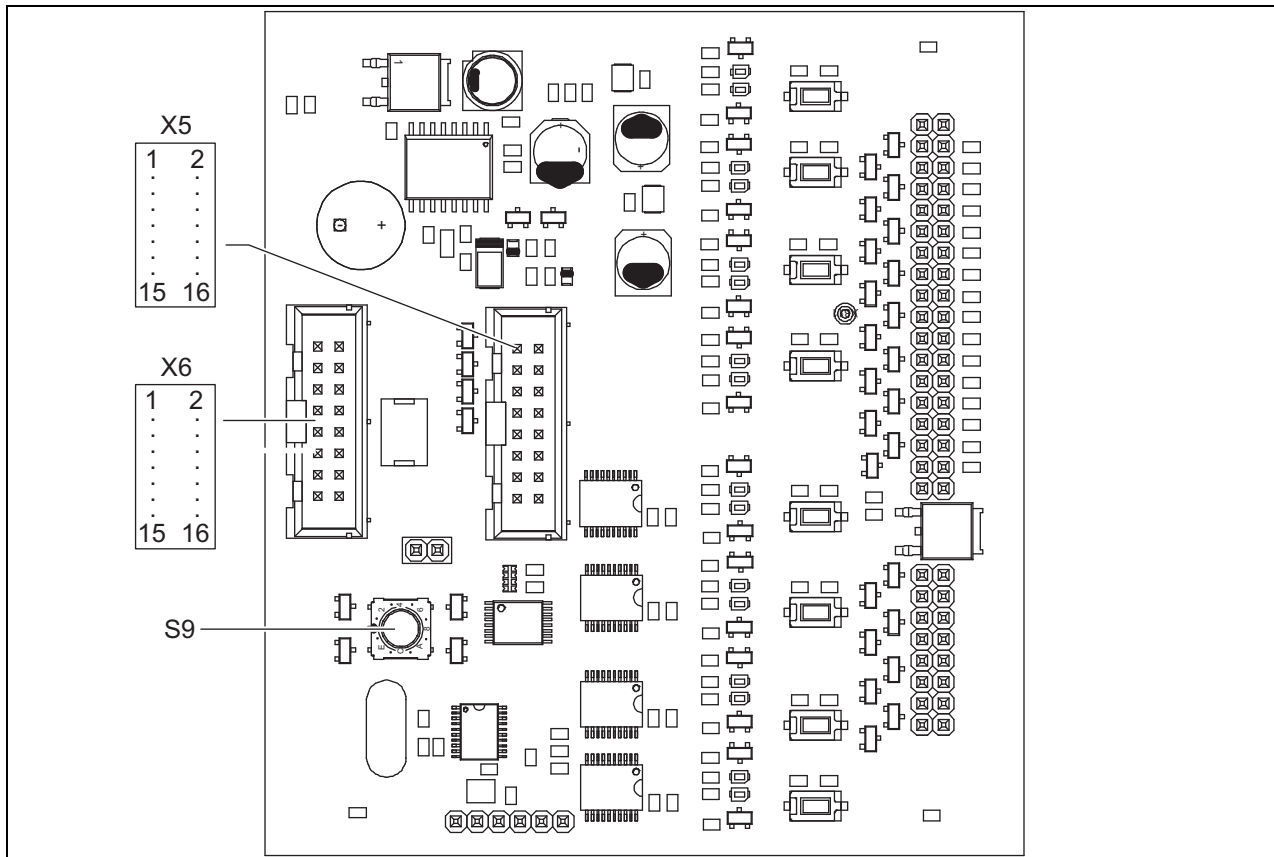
PRS-CSKPM 구성부품 측면 PCB
